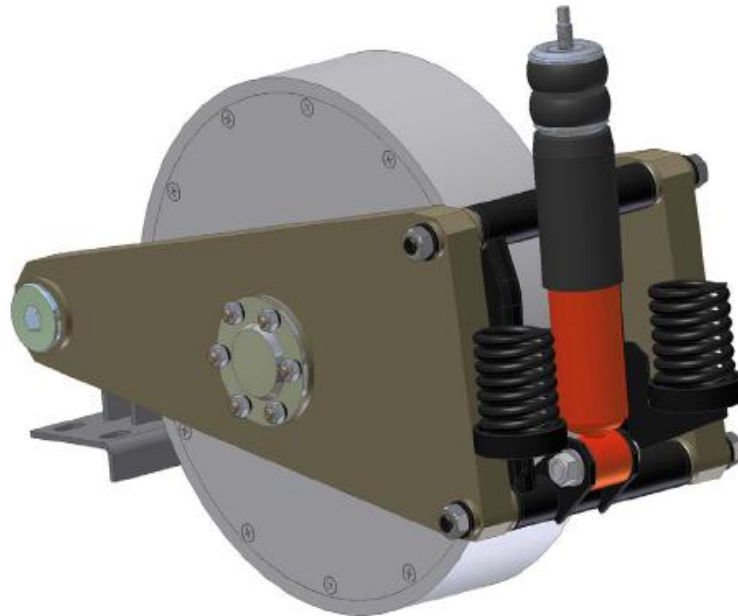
Блок подвески опорного и ведущего колеса юнибуса Ю-325П
